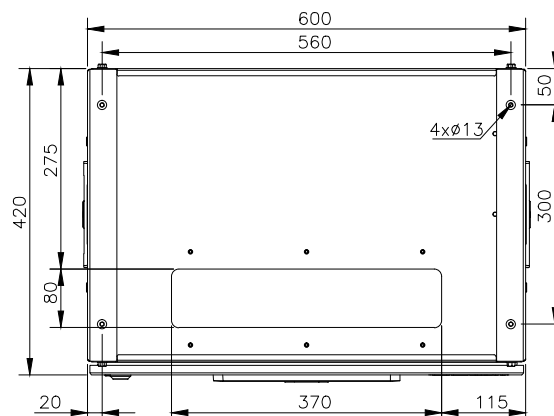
Detalles de fijación AFW Tamaños A, B, C y D
